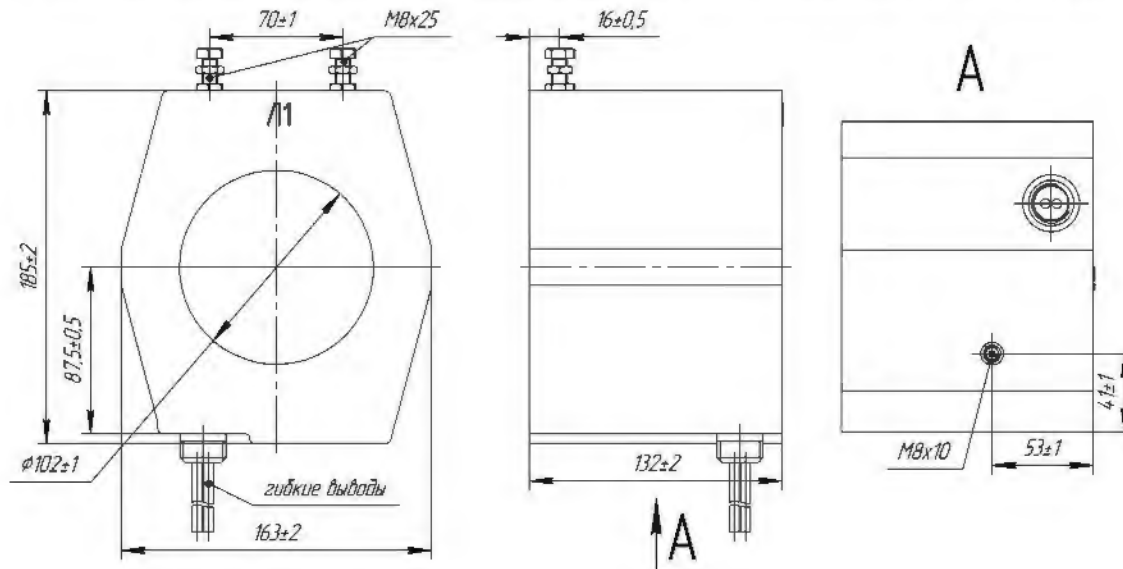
Габаритные и установочные размеры шинного трансформатора ТШ-ЭК-0,66 М9.
